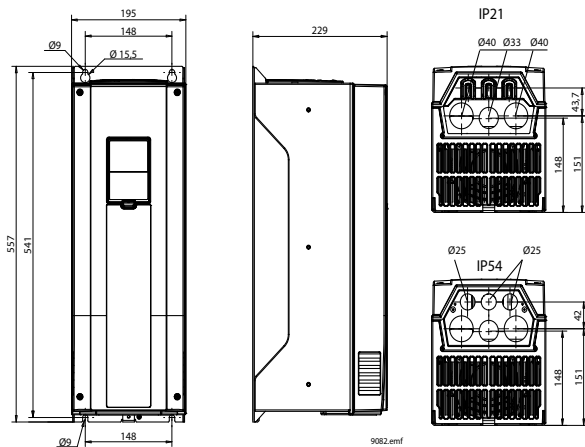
Dimensões do inversor de CA Praxi, MR6, montagem na parede
